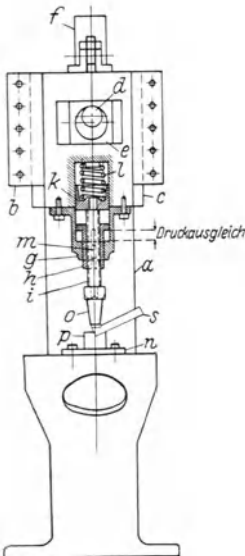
Schweißvorrichtung, aus einer alten Lochstanze hergestellt.
